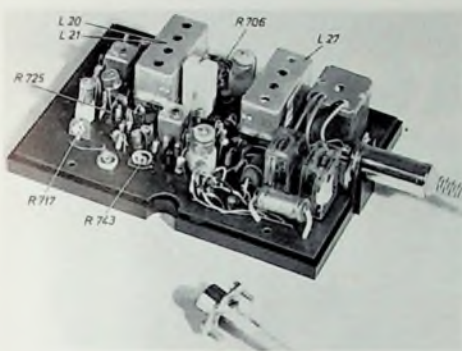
Printplatte des Adapters mit Abgleichpositionen und Verlängerungskabel
